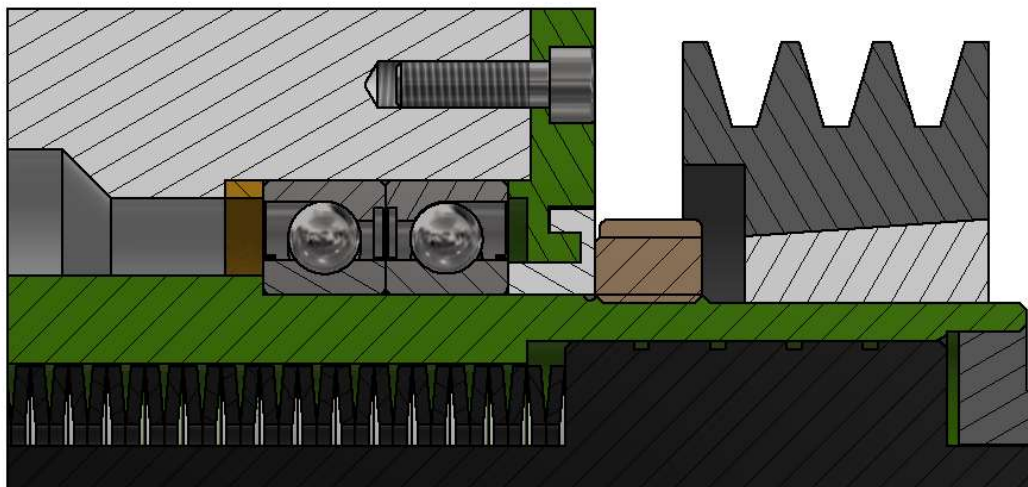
Řez vřeteníkem s odepínací jednotkou
